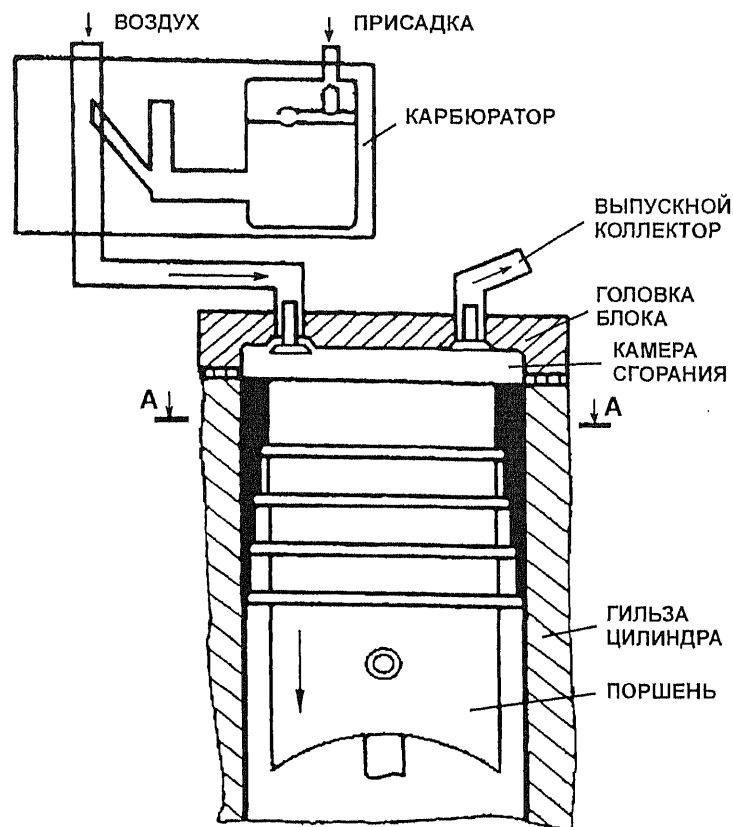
Схема способа повышения качества приработки деталей ЦПГ двигателя
